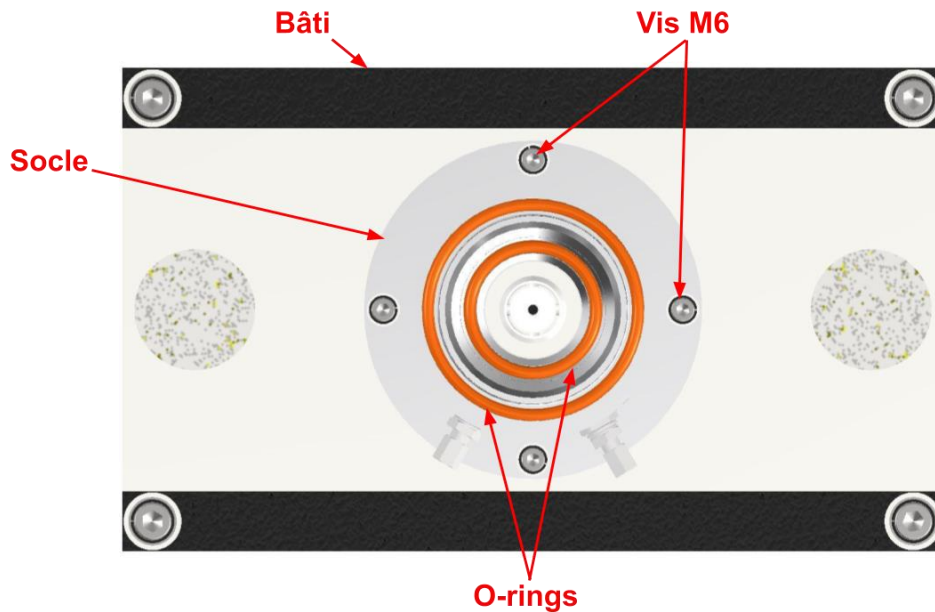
Vue de dessus du socle de la pièce à tester (sans pièce)
